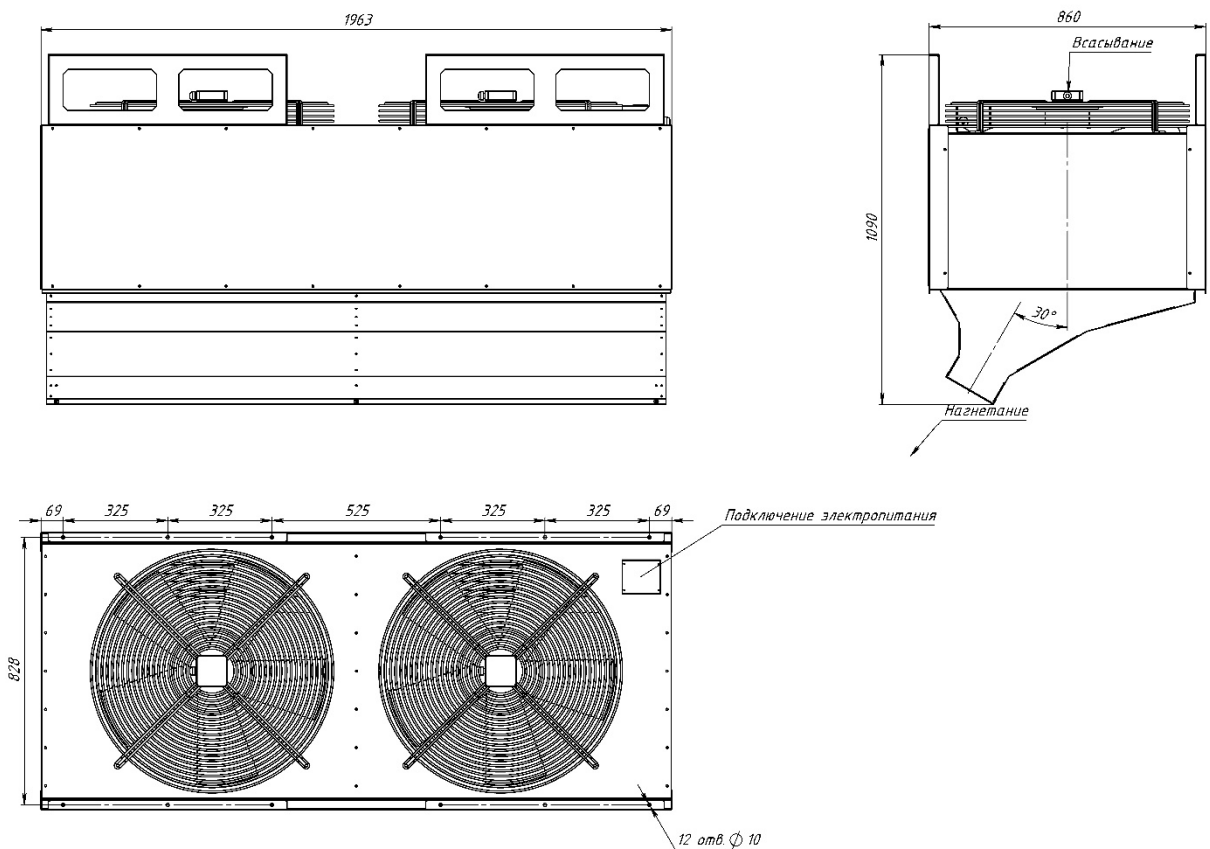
Габаритные и присоединительные размеры SA1 16500 Z (левое исполнение)
